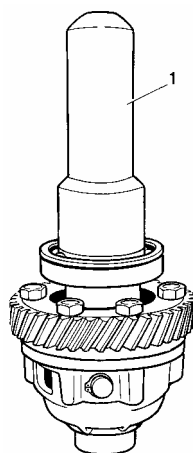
Напрессовка подшипника на корпус дифференциала:
